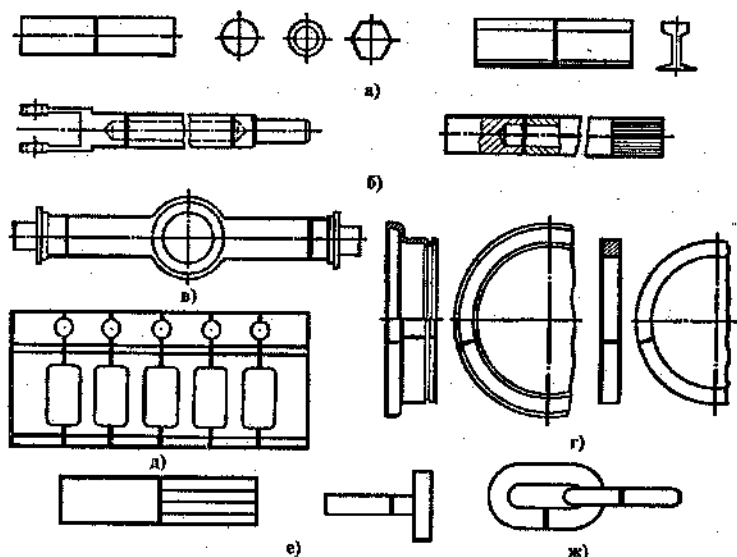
Примеры узлов, выполненных стыковой сваркой:
